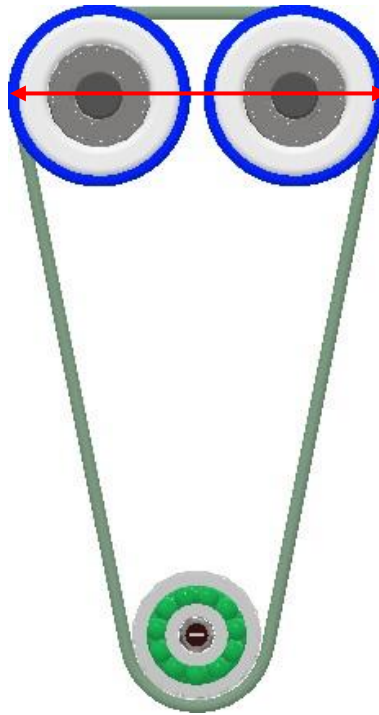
Vista frontal del sistema de transmisión rodillo-conjunto de ruedas
